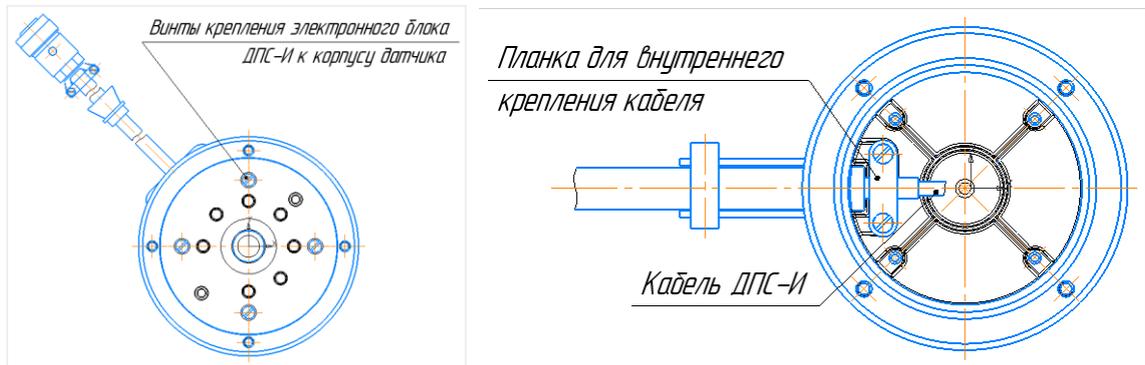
Место расположения креплений электронного блока и крепление кабеля внутри датчика
